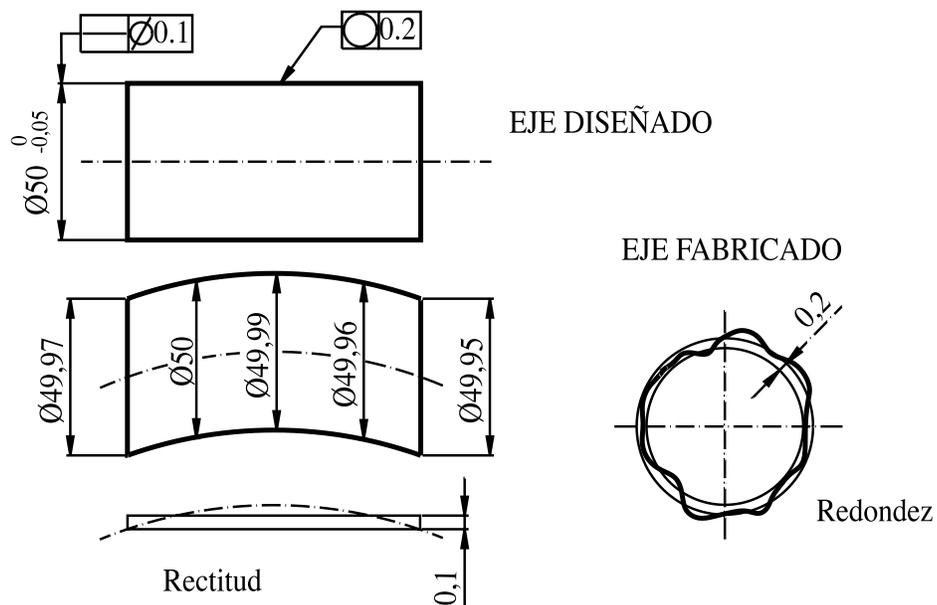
Indicación de tolerancias dimensionales y geométricas en un eje cilíndrico.
